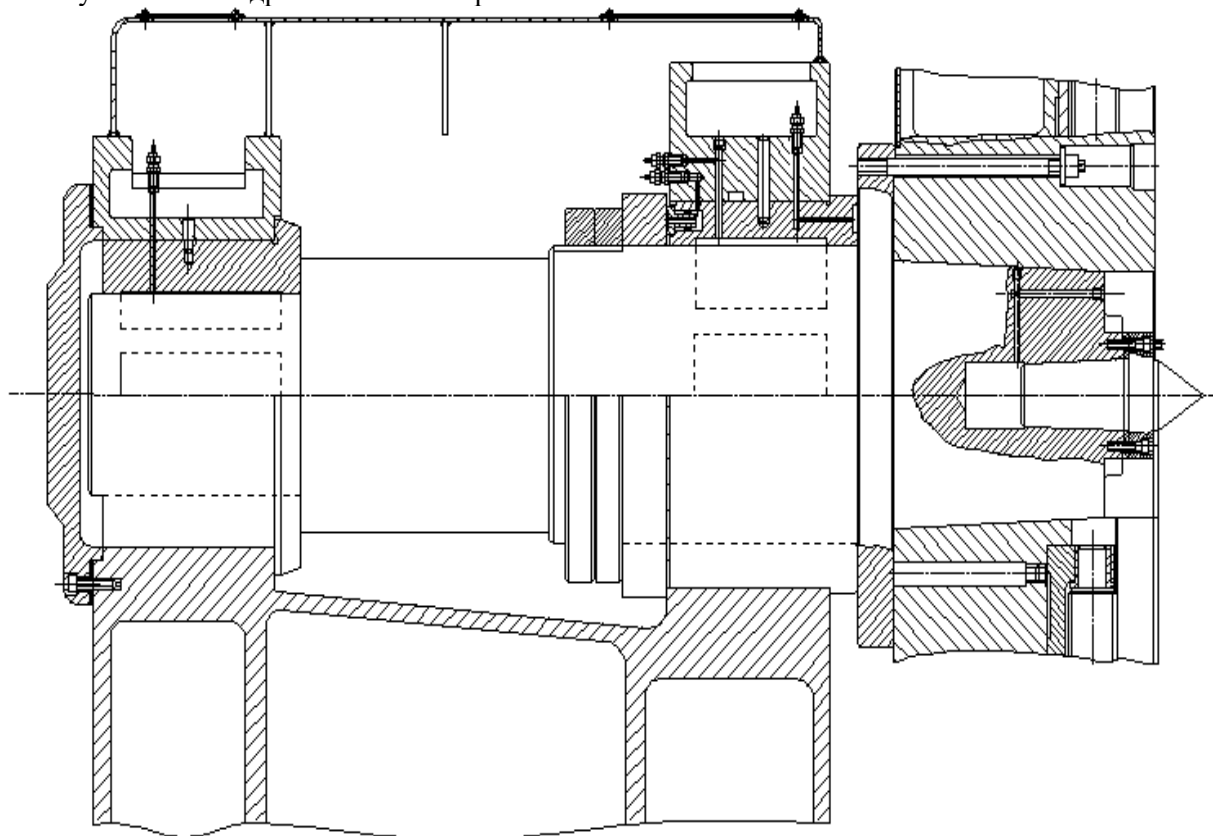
Шпиндельний вузол важкого токарного верстата з радіально-упорними гідростатичними підшипниками
